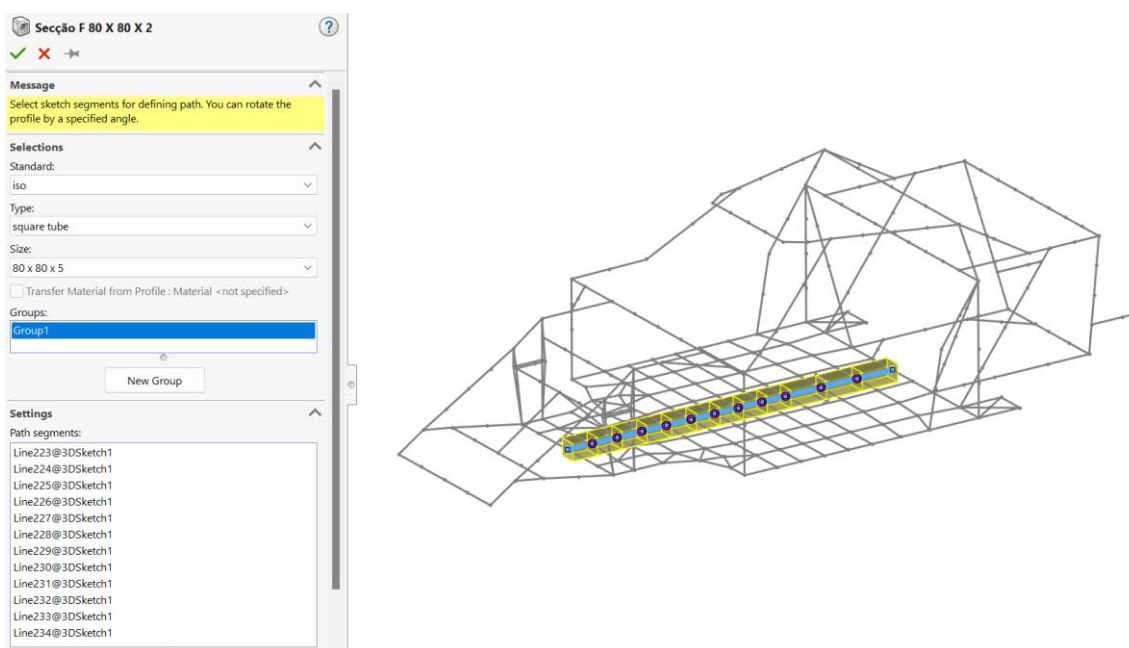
Configuração da viga F como exemplo para a criação dos elementos de viga tridimensional elástica, com recurso à ferramenta “*Structural Member*”.
